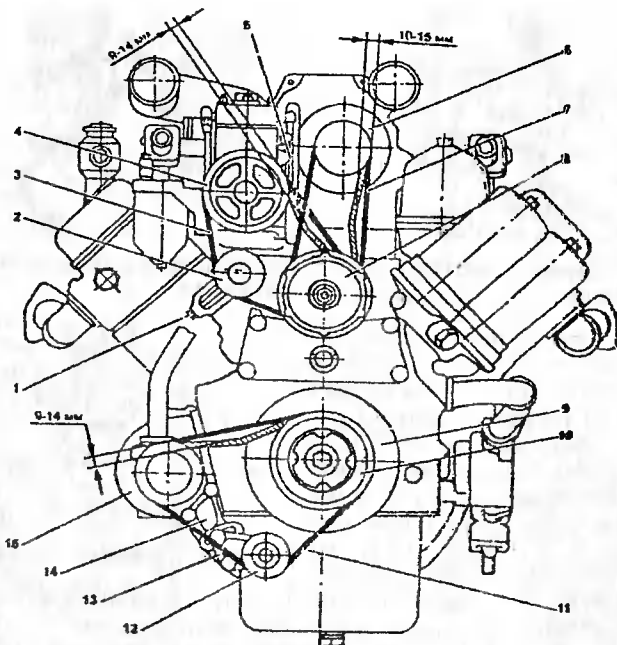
Проверка натяжения ремней привода агрегатов (ЯМЗ-7511.10):
